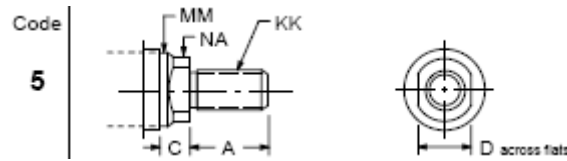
Dimensiones del final de vástago código 5, para cilindro compactador principal.
